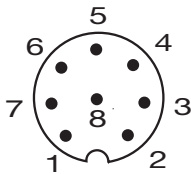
Pinbelegung BKS, Steckverbindung am BIW
